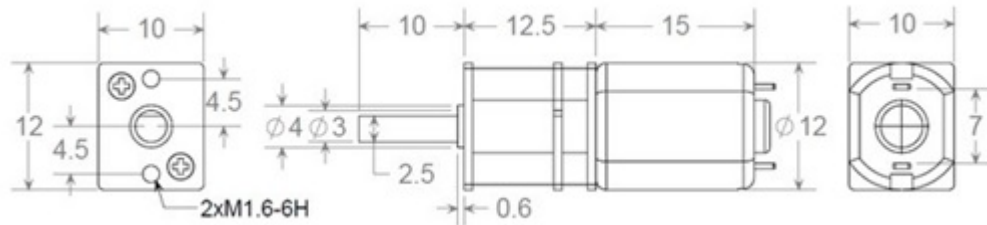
Dimensiones del micro-motor Pololu 1000:1 (unidades en mm).
